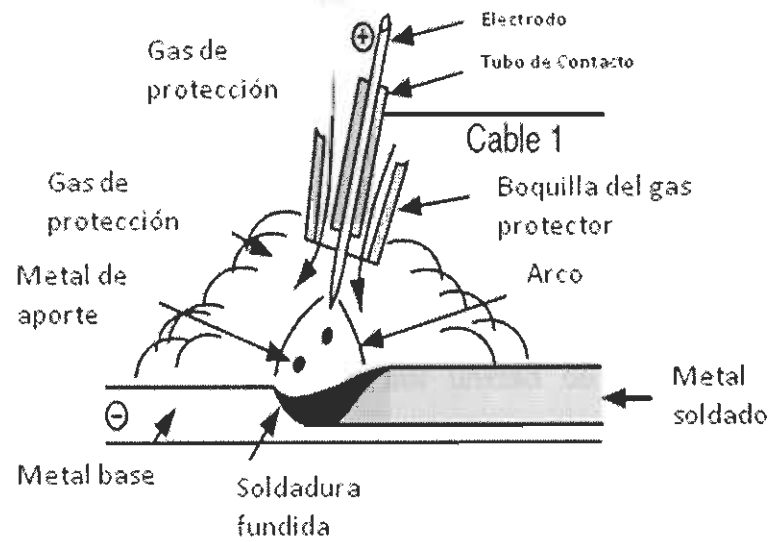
Detalle de la zona de la soldadura [2].
